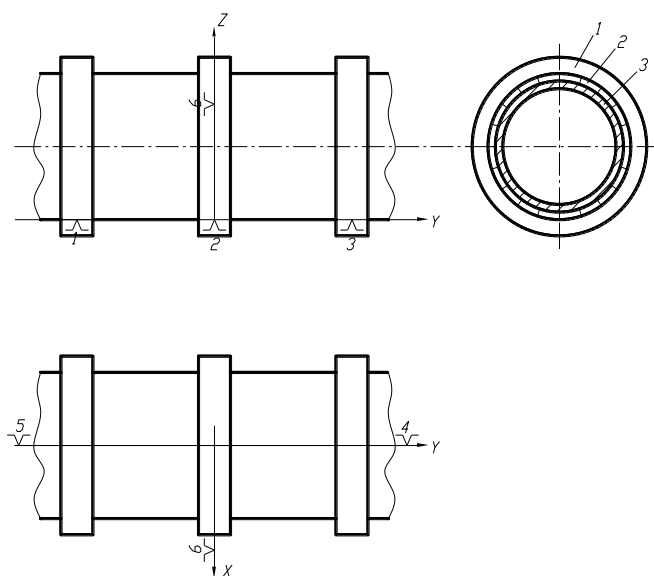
Схема базирования корпуса вращающегося агрегата:
